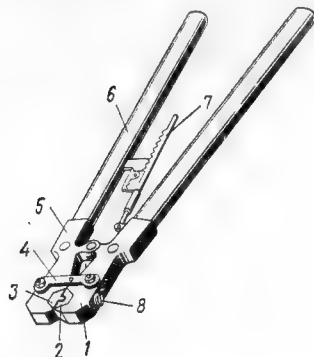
1 — рычаг; 2 — матрица; 3 — пуансон; 4 — планка; 5 — вилка; 6 — рукоятка; 7 — устройство блокирующее; 8 — винт
